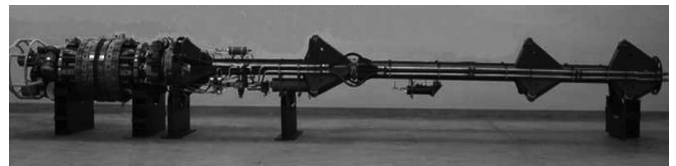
Машина для контактной стыковой сварки стыков труб
